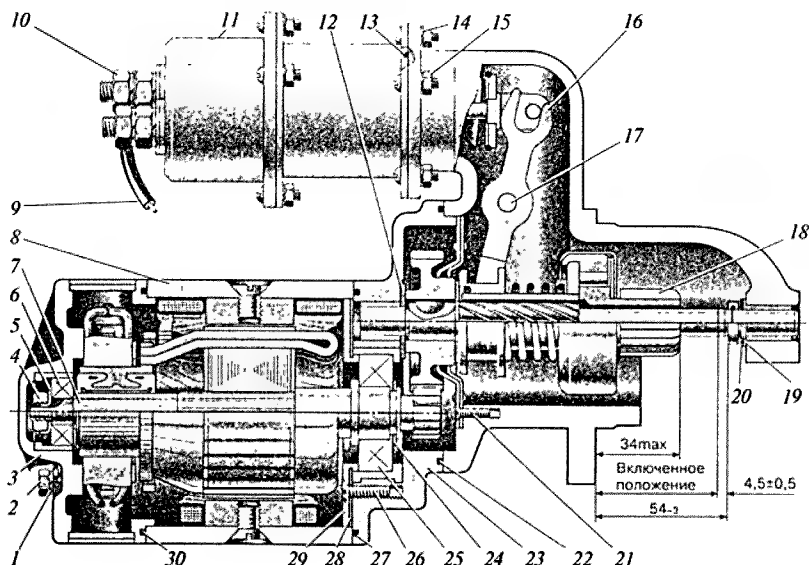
Конструкция стартера со встроенным цилиндрическим редуктором с внешним зацеплением [1] :
